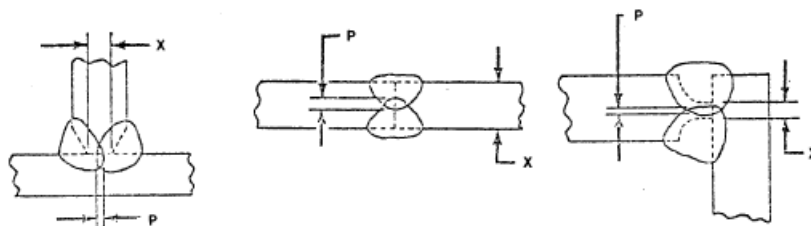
Penetración de solape en soldaduras a tope realizadas por ambos lados [13]
